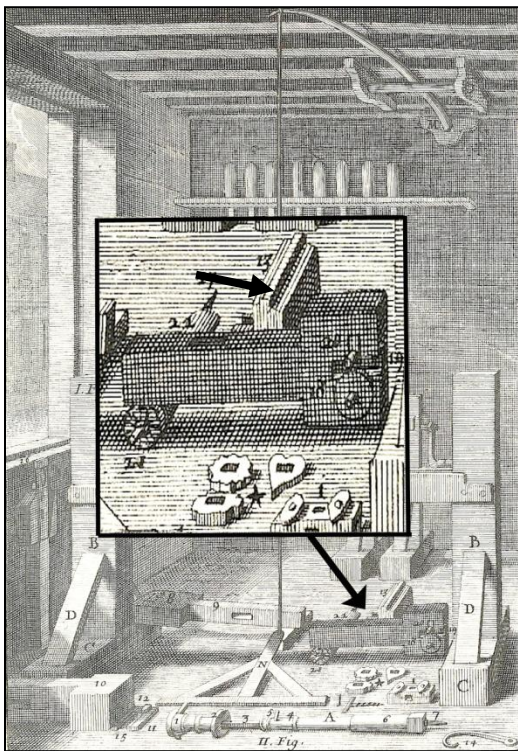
Anlæg (13) gemt under drejebænkens bagdøkket (se pil), Planche LX detalje (efter Félibien, 1676) ingen tegnforklaring
